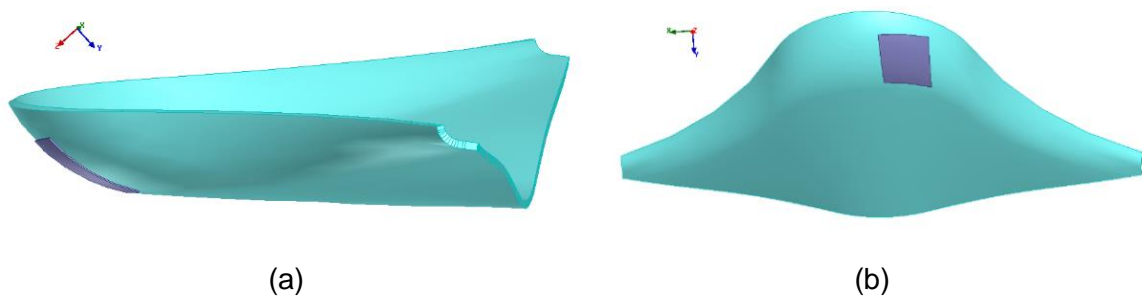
Plano de masa conformado visto desde: a) plano YZ, b) plano XY.
